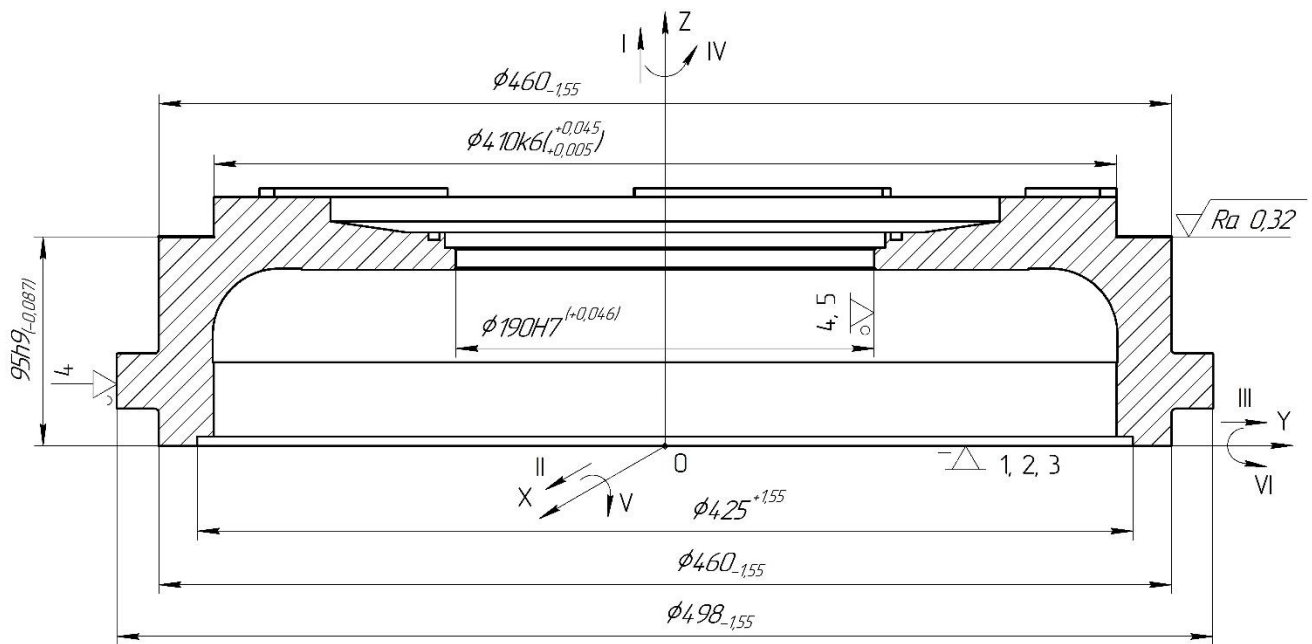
Схема базування заготовки на операції 040. Установ Б
